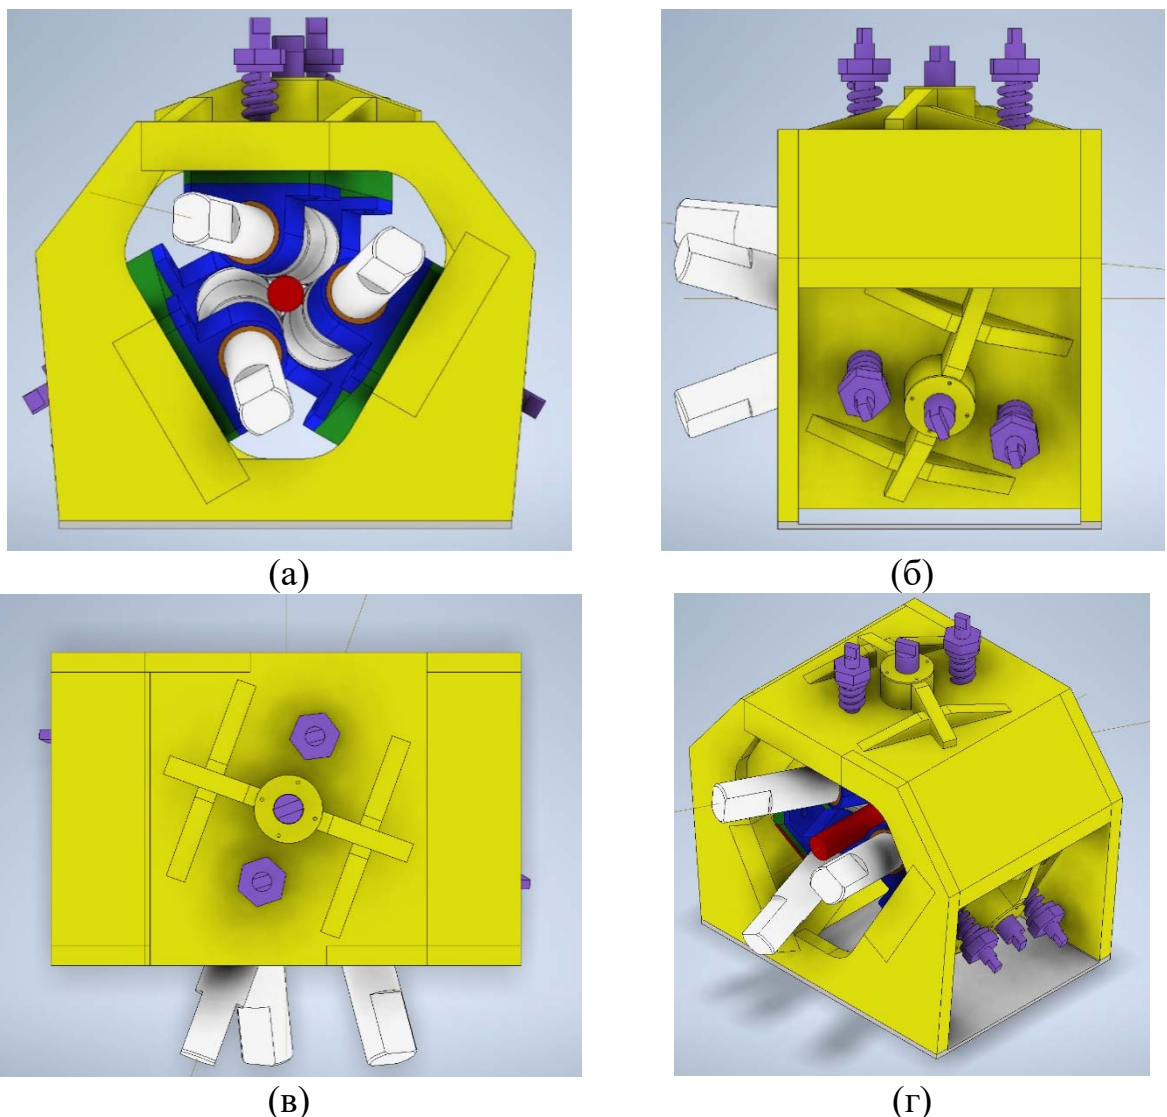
Общий вид 3D модели рабочей клетки: (а) – вид спереди (входная сторона); (б) – вид сбоку; (в) – вид сверху; (г) – изометрия.
